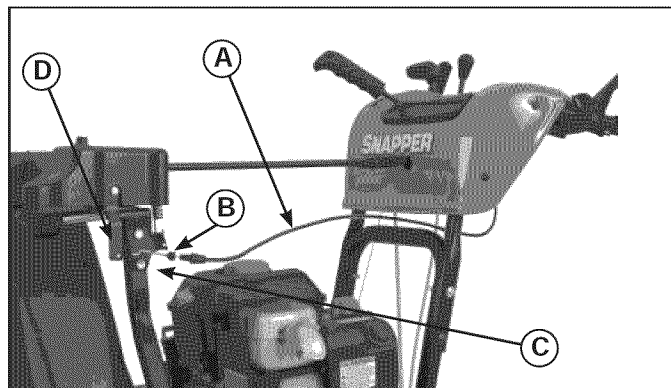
Cable del freno del dispositivo de rotación del vertedero
